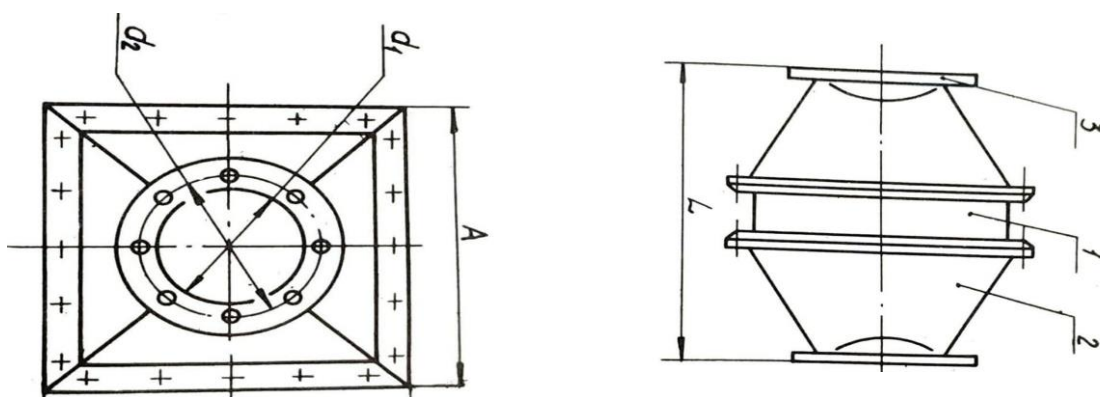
Конструкция магнитного устройства УМО -1000 - 7,5 [6].
